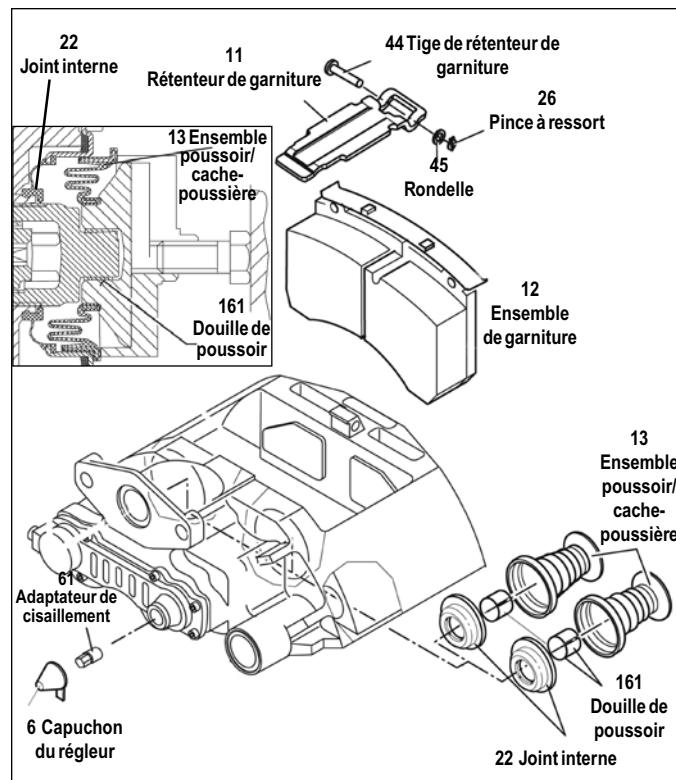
VUES EXPLOSÉE ET EN SECTION DE L'ADB
